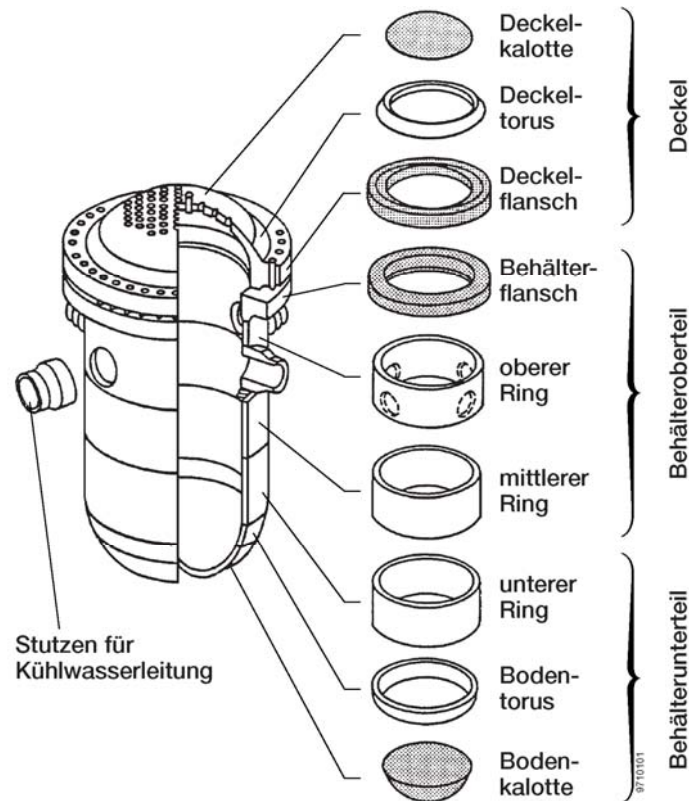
Reaktordruckbehälter einer älteren Siemens/KWU-Anlage mit DWR; schematische Übersicht über die Schmieringe und Kalotten mit Lage der Schweißnähte
